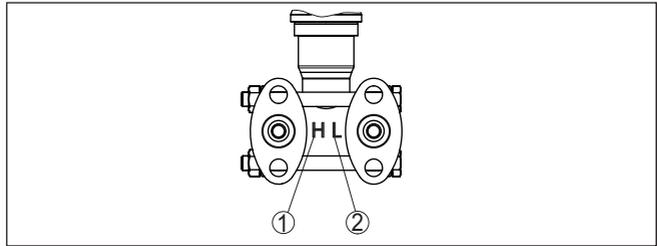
Kennzeichnung für Hoch-/Niederdruckseite an der Prozessbaugruppe
